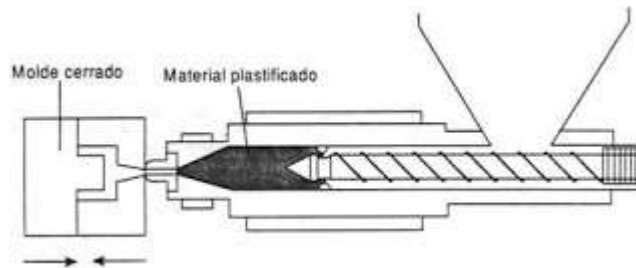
Cierre del molde e inicio de la inyección [5]
